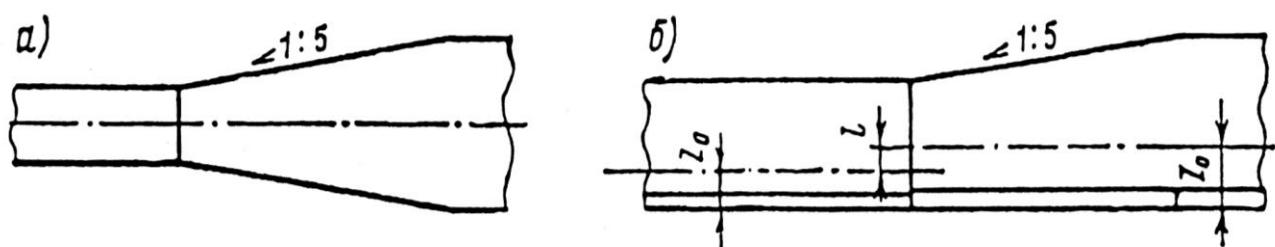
Подготовка стыкового соединения при сварке элементов конструкции разной ширины
